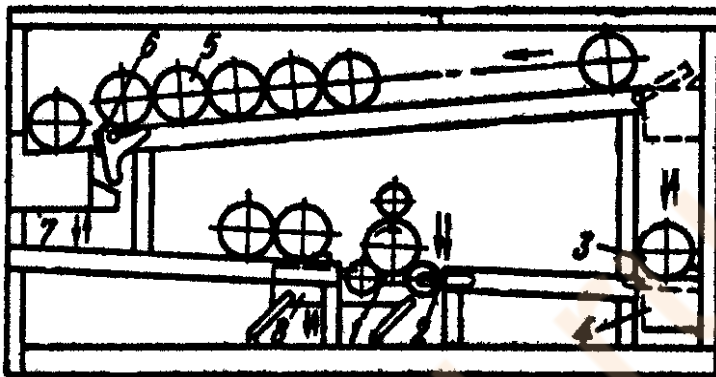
Схема вертикально замкнутой поточной линии для центробежной отливки труб:
